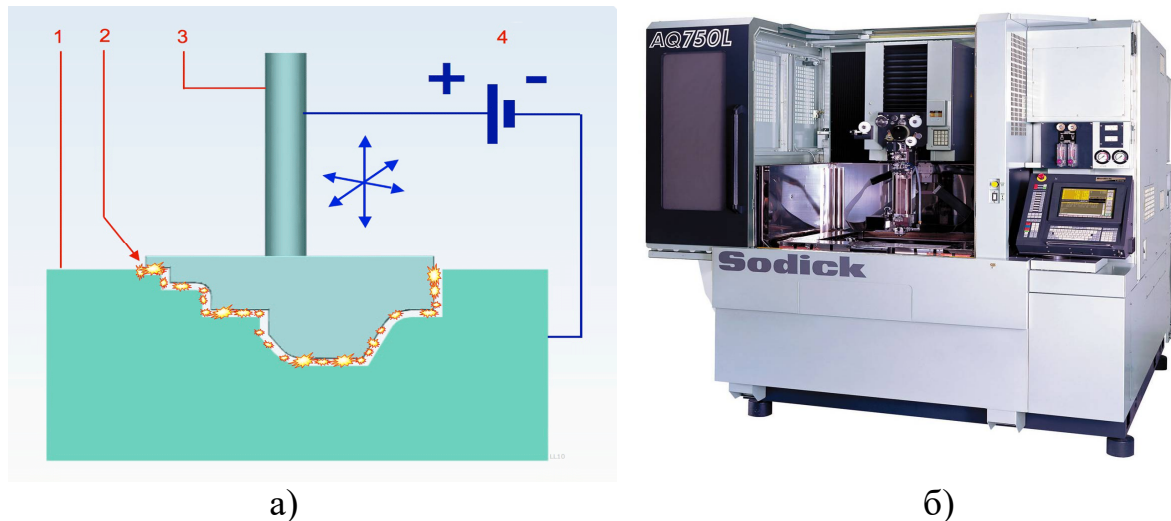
Схема електроіскрової обробки (а) та загальний вигляд електроіскрового верстата: 1 – заготовка; 2 – електричні розряди в зазорі; 3 – інструмент; 4 – генератор електричних імпульсів
